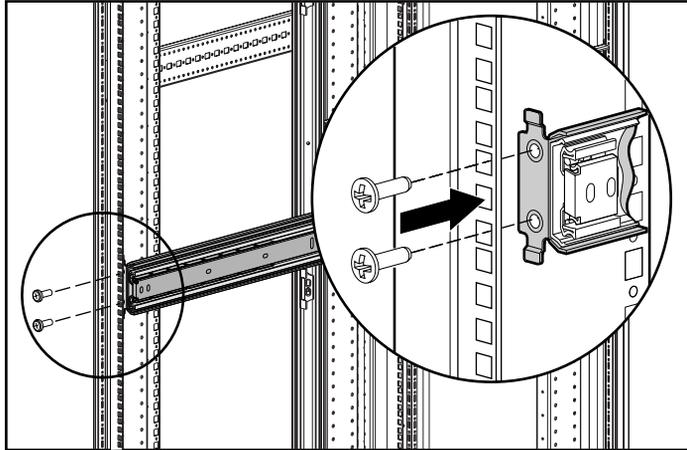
Fixation de l'avant de l'assemblage support de montage
